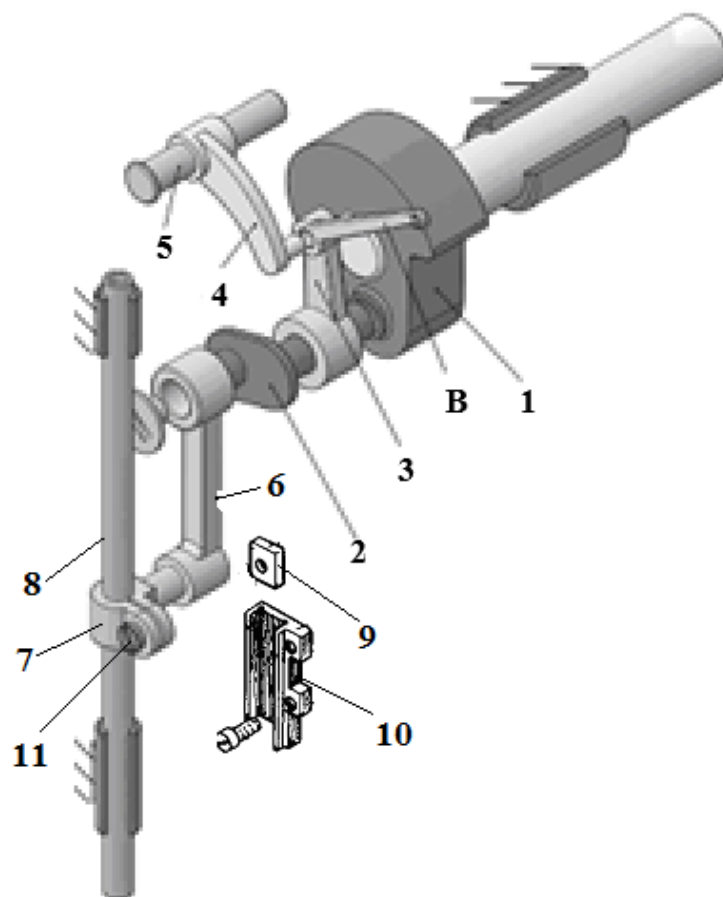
Конструктивна 3D- схема кривошипно-коромислового механізму ниткопритягувача та кривошипно-шатунного механізму голки
